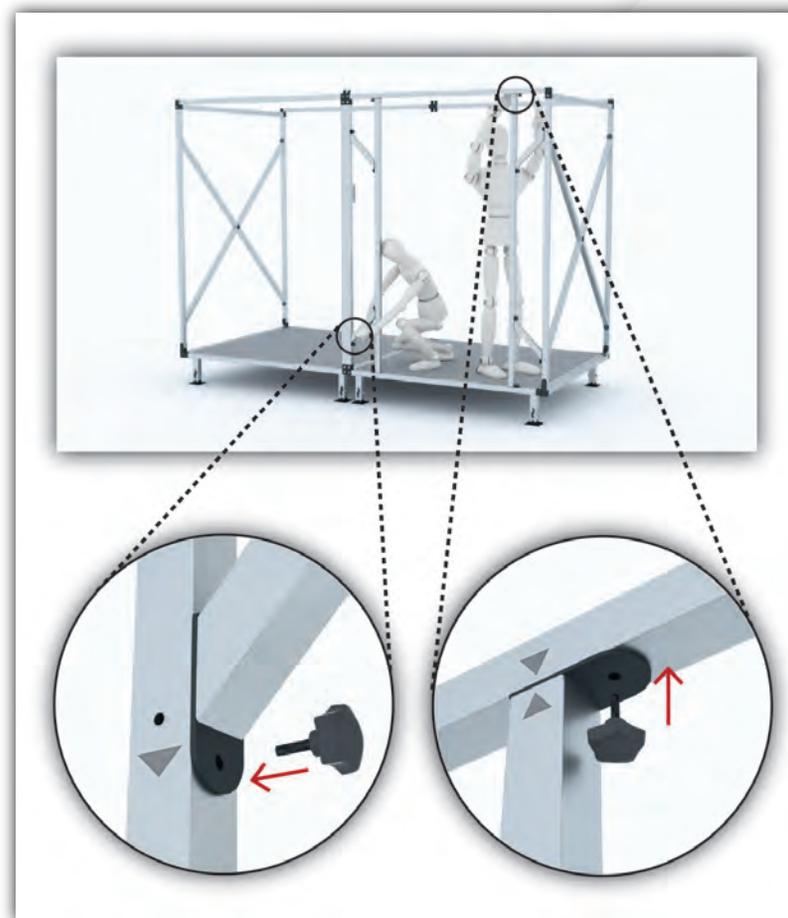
Ensamblaje de soportes de puerta con columna central y muros por medio de tornillos con empuñadura.
